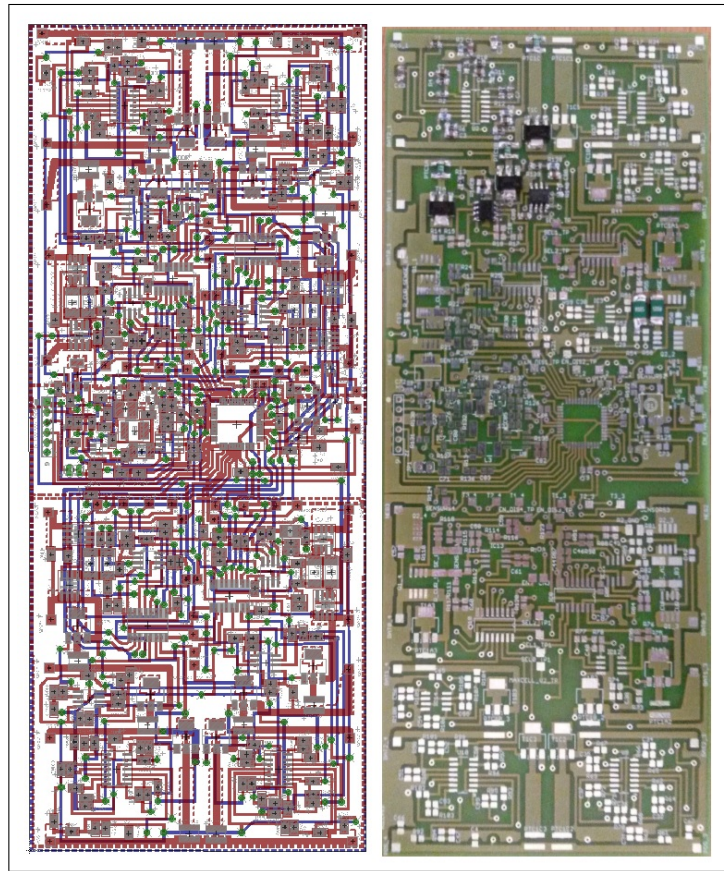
Dimensões da PCB. ( $h=200\text{mm}$  e  $l=80\text{mm}$ )
